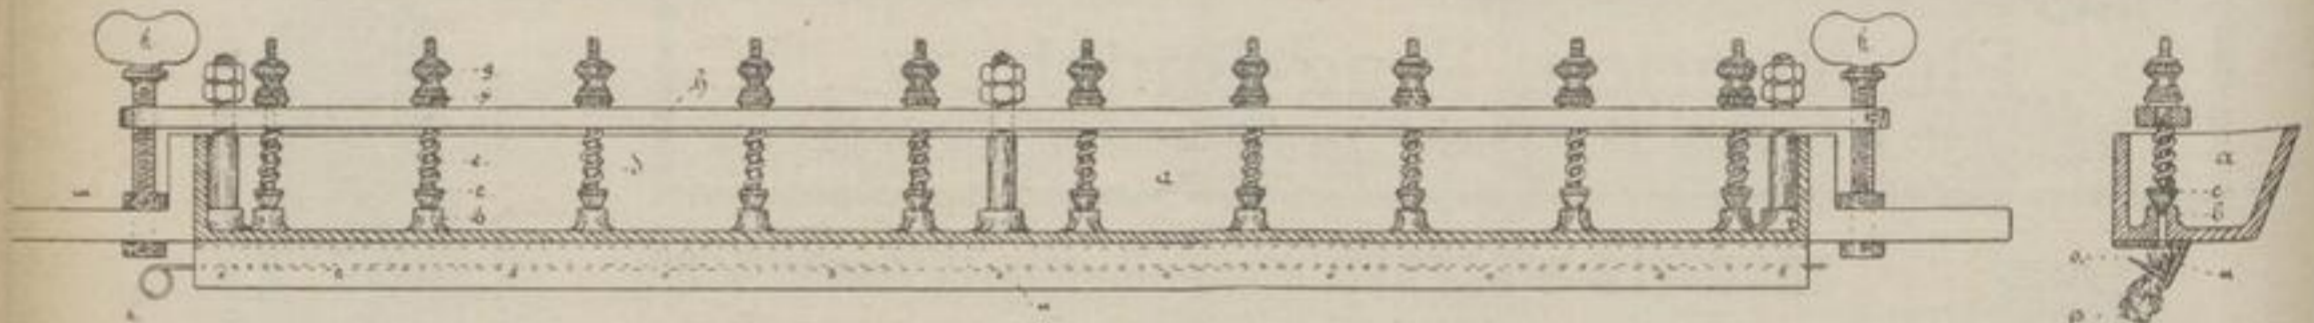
(Befeuchtungs-Apparat für Steindruck-Schnellpressen.)
